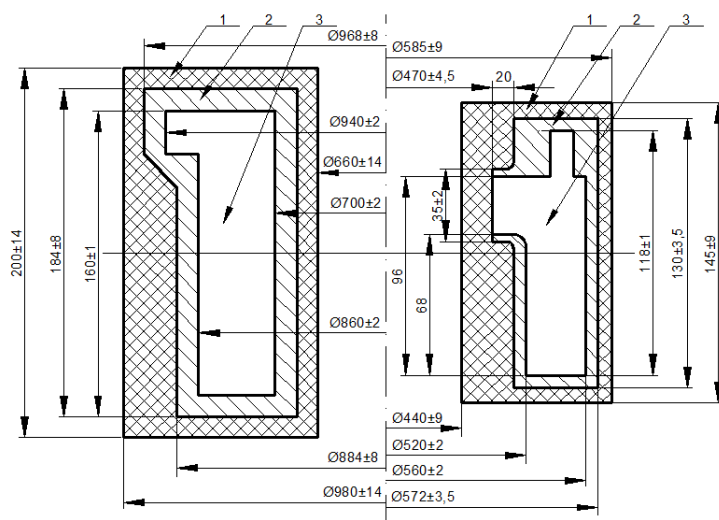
Сечения кольцевых деталей и поковок из сплава 5В (слева) и стали 45:
